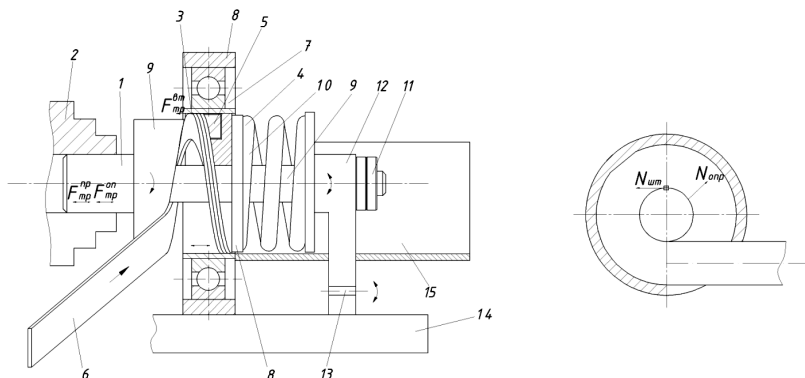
Пристрій для формування ремонтних гвинтових заготовок
